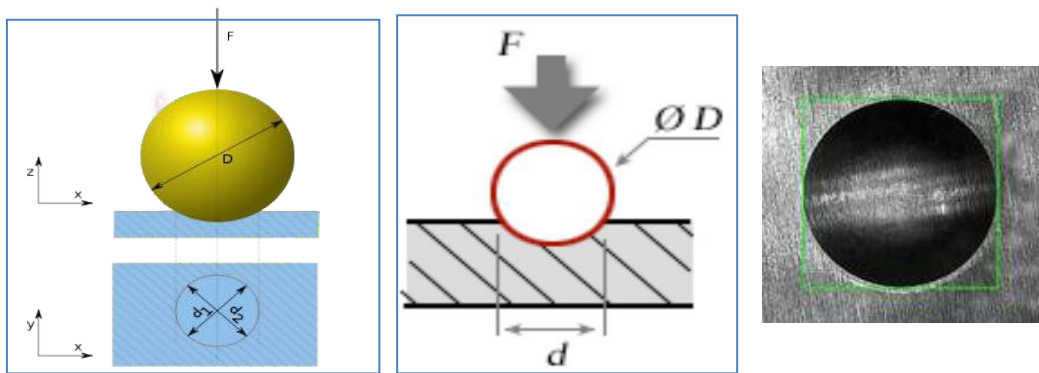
Principe de l'essai Brinell et empreinte typique de l'essai
